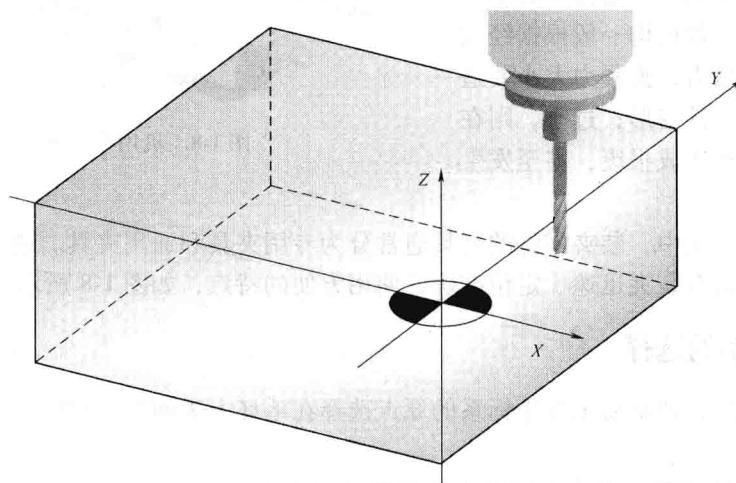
刀具与 Y 轴所在的工件边缘恰好接触
